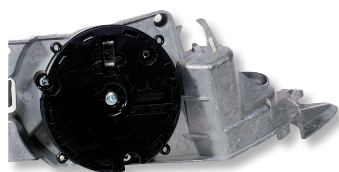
Moteur de rétroviseur assemblé sur boîtier en aluminium.
